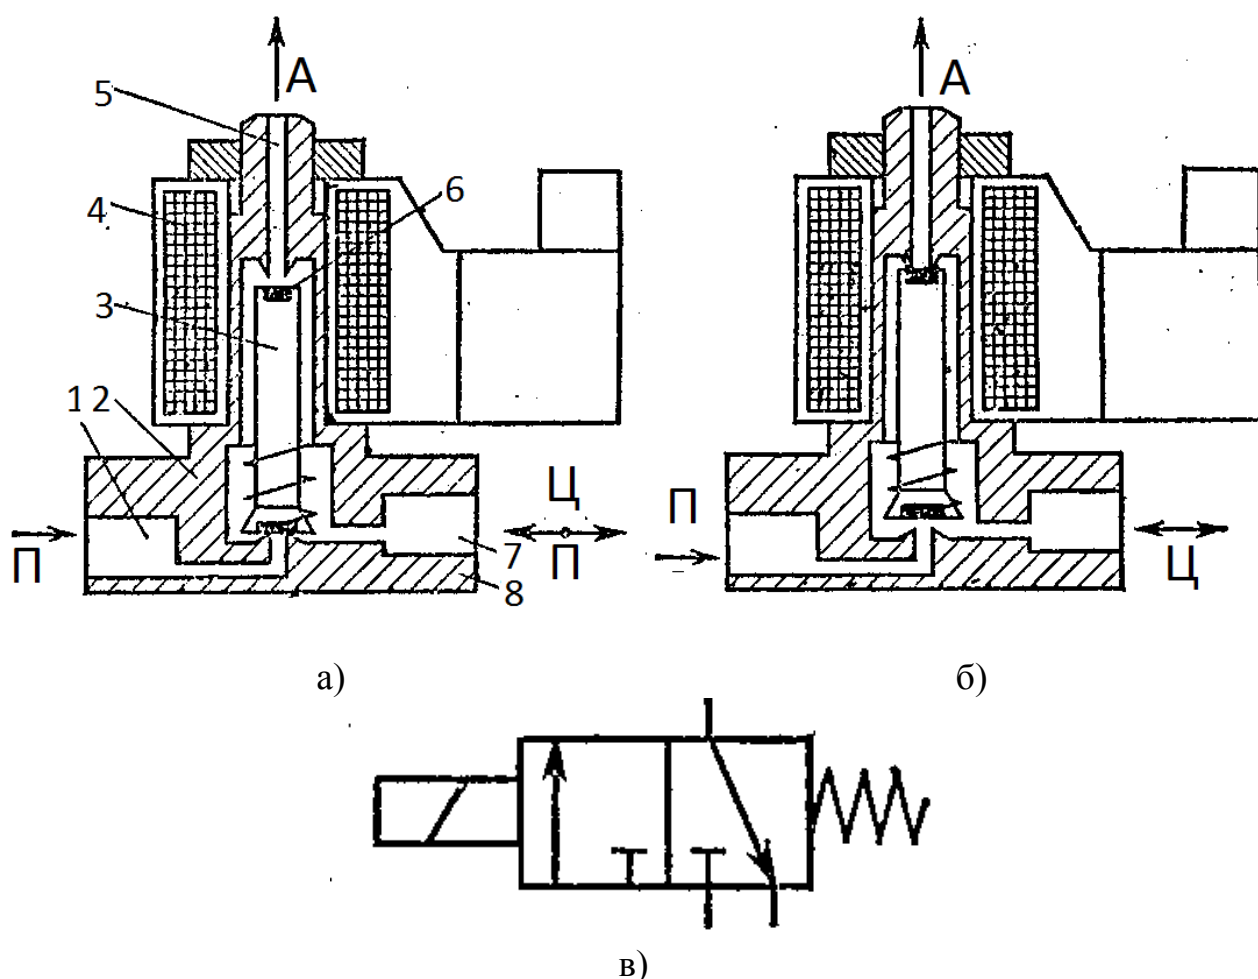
Двухпозиционный трехлинейный пневмораспределитель с электрическим управлением: а), б) конструктивные схемы; в) условное изображение
